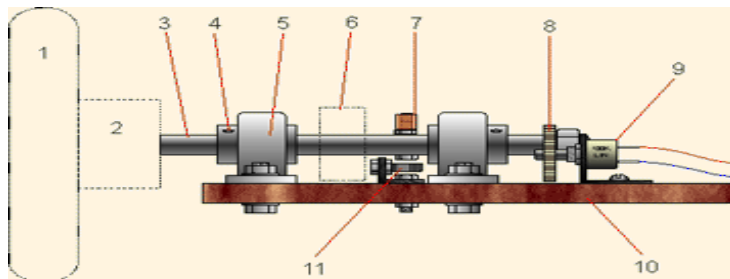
Схема рулевого механизма, где 1 – рулевое колесо; 2 – ступица колеса; 3 – вал (болт 12мм x 180мм); 4 – винт (держит подшипник на валу); 5 – 12мм подшипник в опорном кожухе; 6 – центрирующий механизм; 7 – болт-ограничитель; 8 – шестерни; 9 – 100к линейный потенциометр; 10 – фанерная основа
